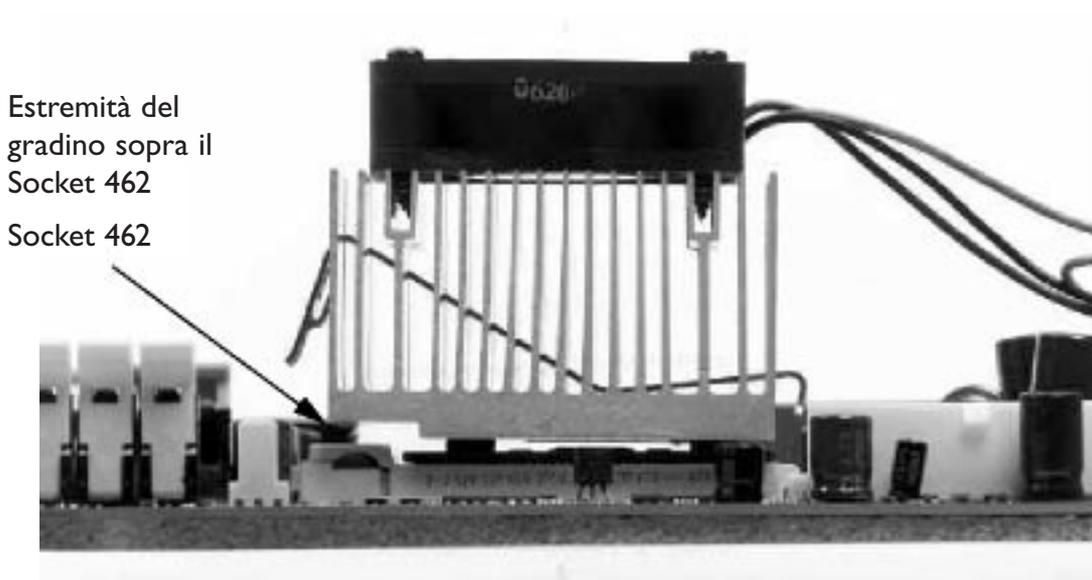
La maniera corretta di installare il dissipatore sul processore.
